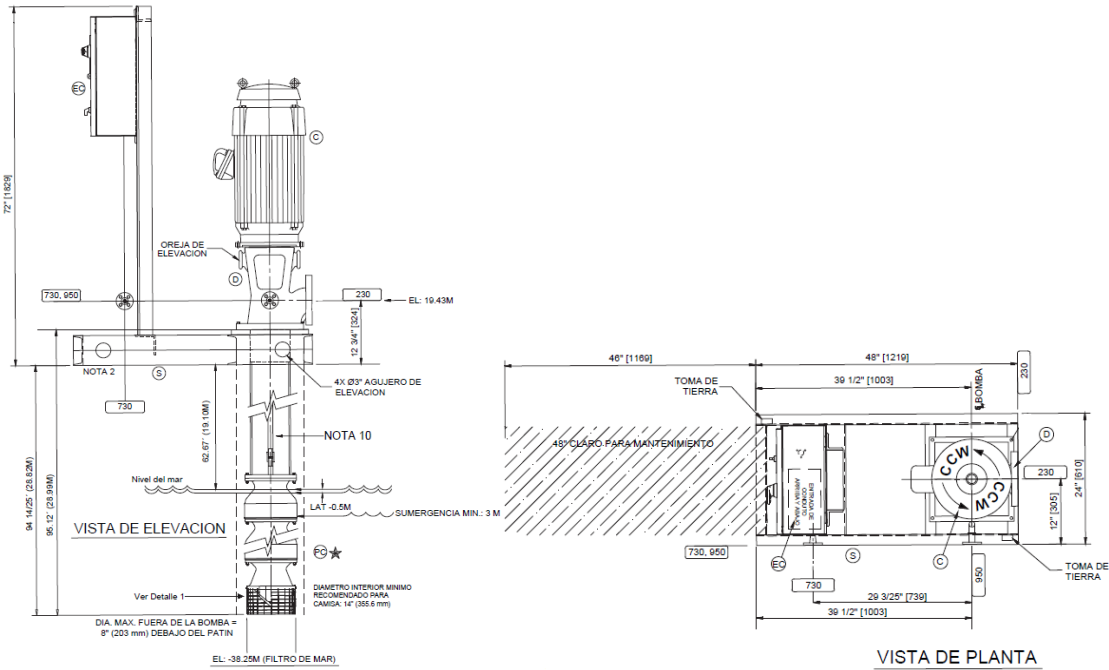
Plano dimensional para bomba jockey; tomado de Peerless Pump <http://www.pumptech.com.mx/sistemas-contra-incendio-peerless.htm> .
